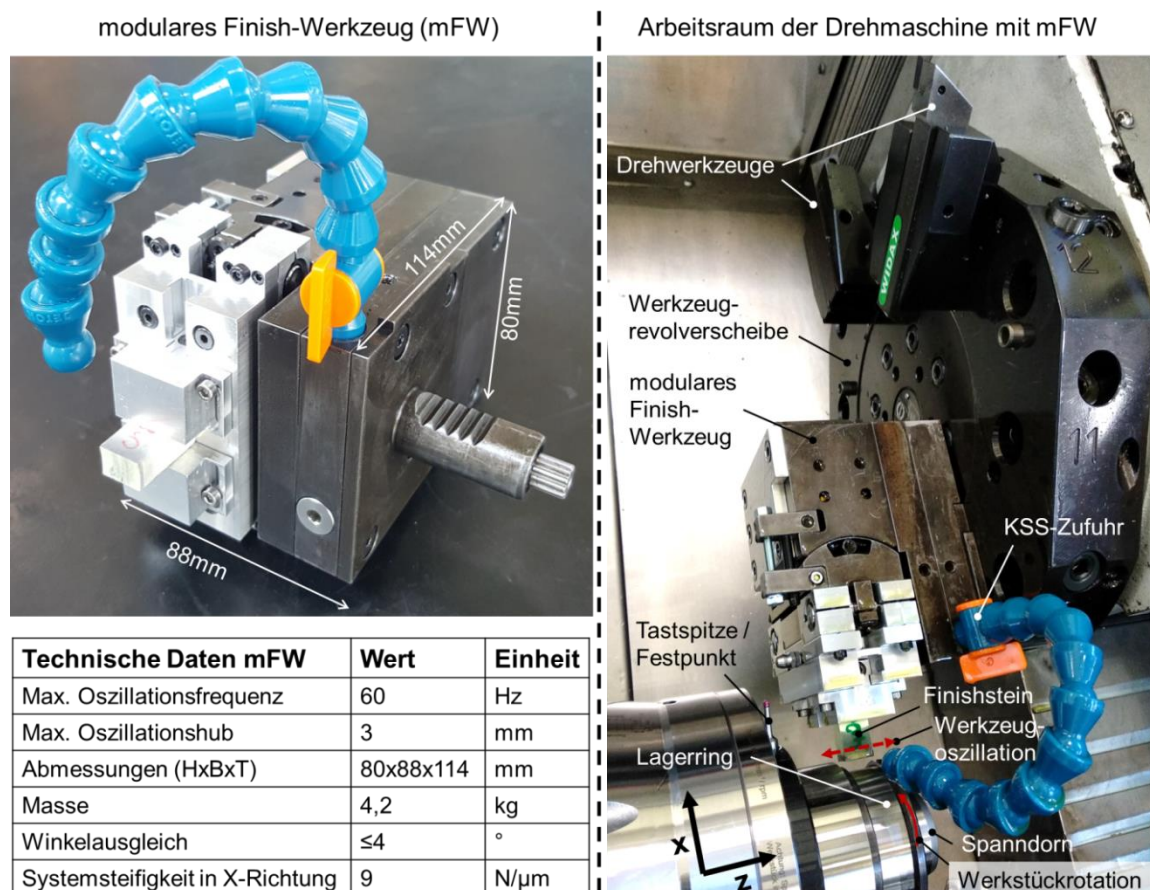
Arbeitsraum der Drehmaschine Hembrug Mikroturn 100 mit modularem Finish-Werkzeug
